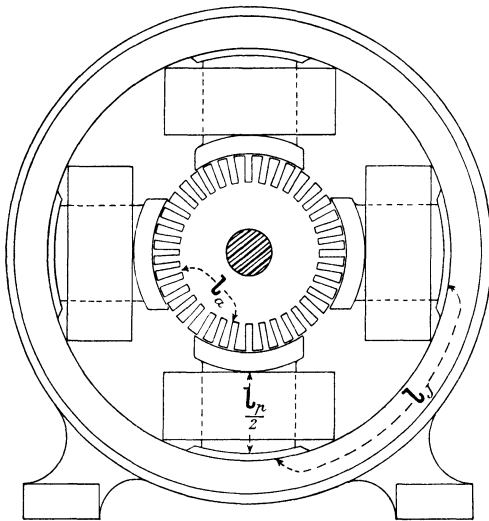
Vierpolige Maschine. Maßstab 1 : 6.
